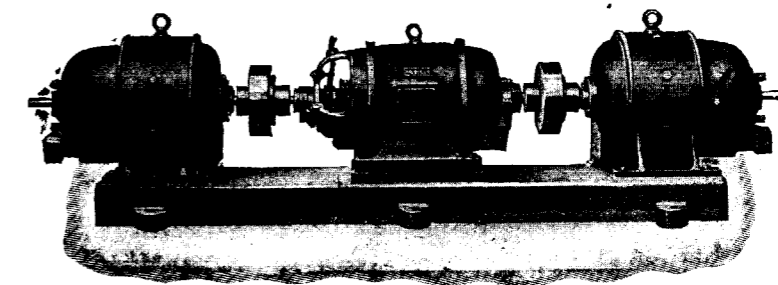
ª—Grupo con dos dinamos (2 x 200 amp.) para soldadura por arco accionadas por un motor trifásico.
